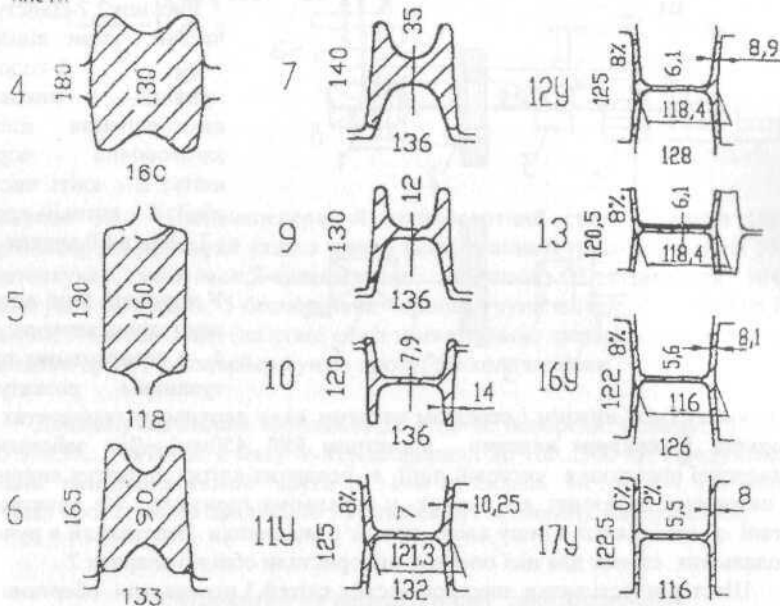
Схема прокатки колонового двутавра 120 DIN
